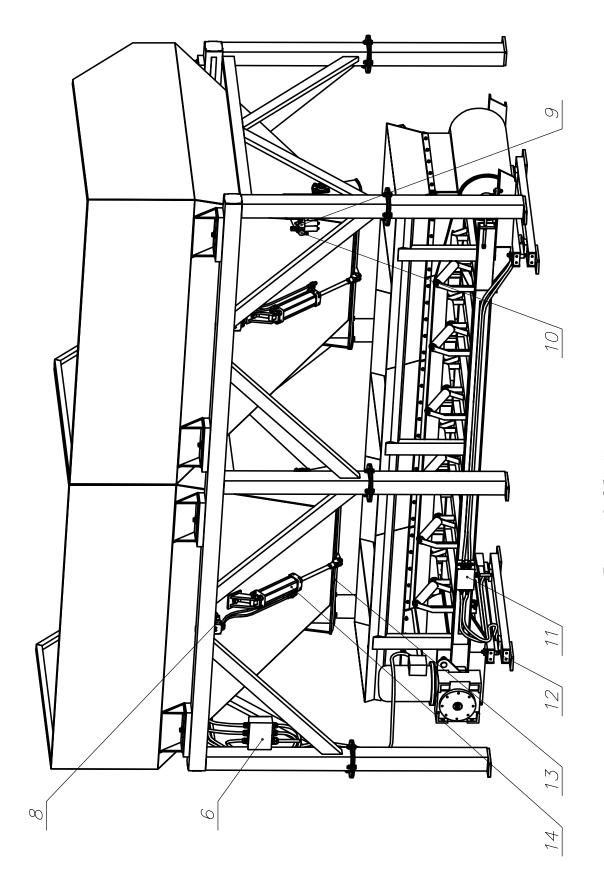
Общий вид дозатора вид спереди. 1 – бункер; 2 – рама; 3 – конвейер взвешивающий; 4 – удлинитель стойки; 5 – удлинитель стойки со скобами; 7 – вибратор; 15, 16 – винты регулровочные.
